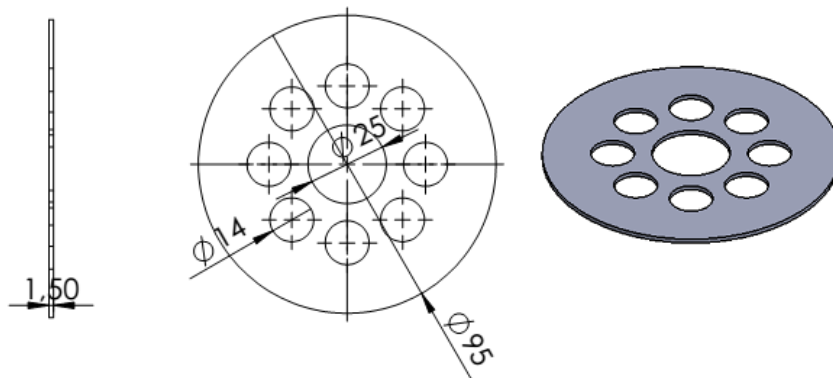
Desenhos dos discos do rotor do segundo protótipo de TMD construído. Dimensões dadas em milímetros.
